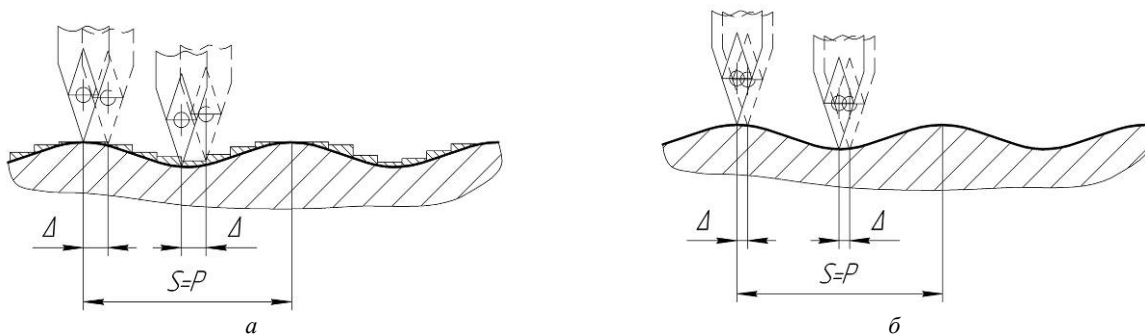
Схема зрізання припуску при точінні внутрішніх різей стандартним різцем: а) чорнова обробка; б) чистова обробка
